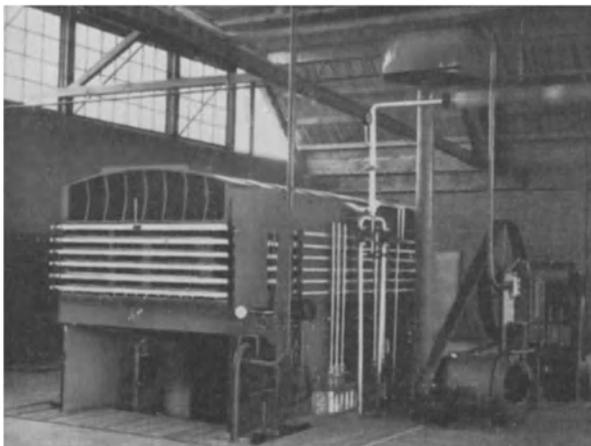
Ansicht einer Sperrplattenpresse (Niederrheinische Maschinenfabrik Becker u. van Hüllen, Krefeld); rechts die Preßpumpe.
